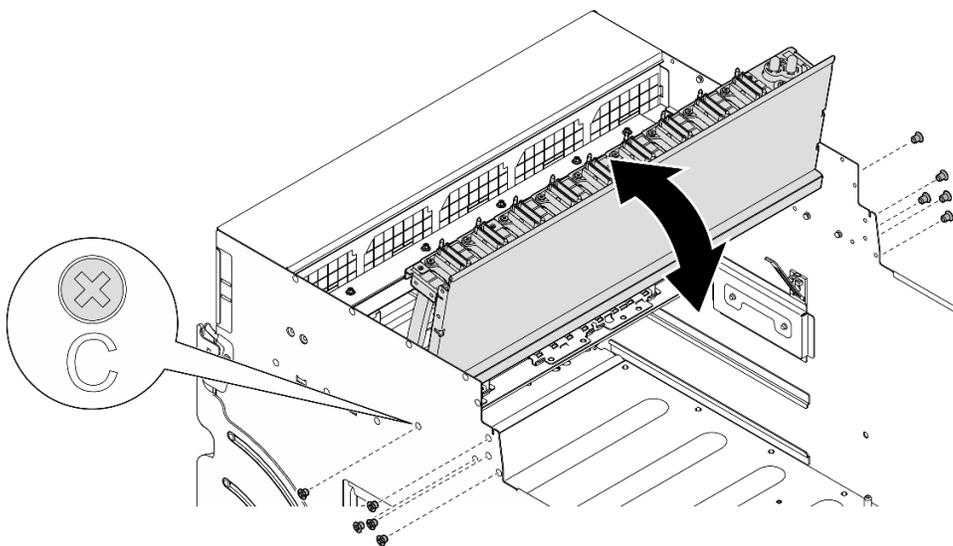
Giro del arnés de cables del conmutador PCIe frontal
